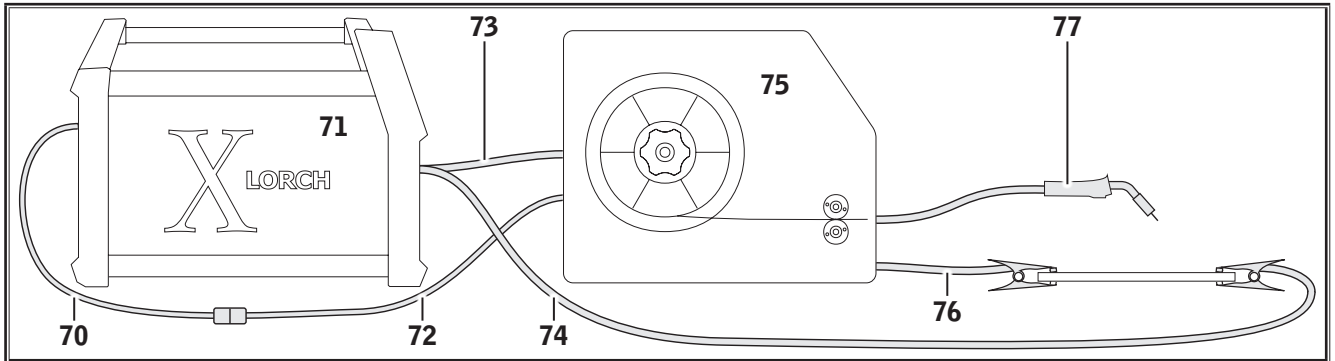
Anschlussschema MSG-Schweißen
